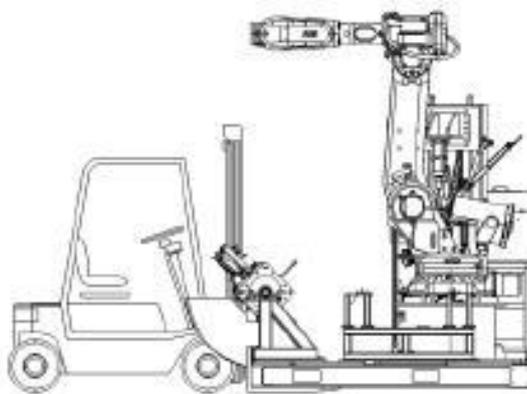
Imagen croquis carretilla elevadora contrapesada cargando un robot.
